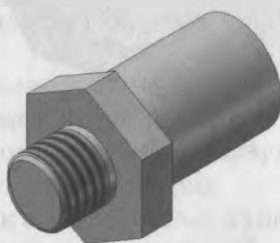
Этап 3. Сформированный под резьбу цилиндрический стержень
